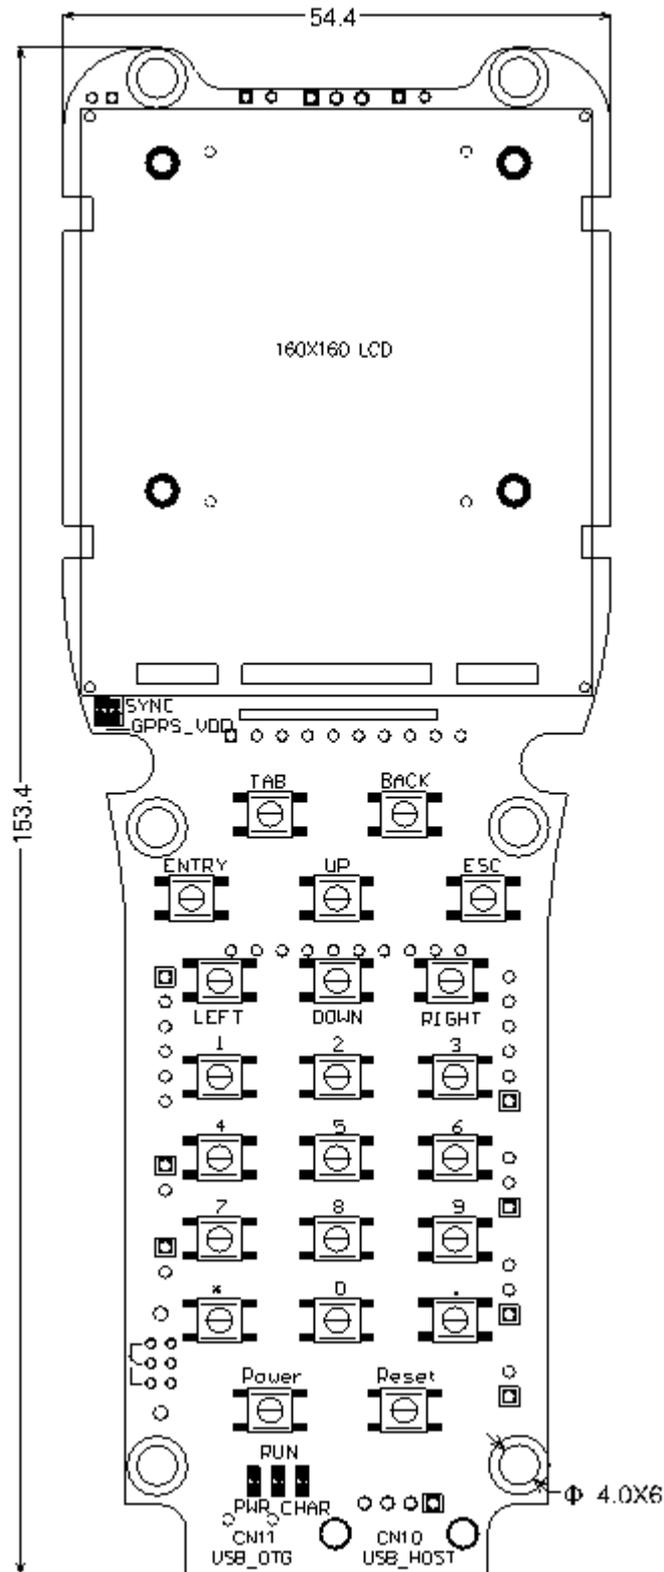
EM9283EVb 顶视图 (标注尺寸: mm)
